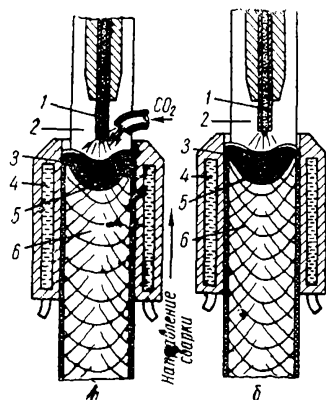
Схема электродугового процесса сварки с принудительным формированием порошковой проволокой:
